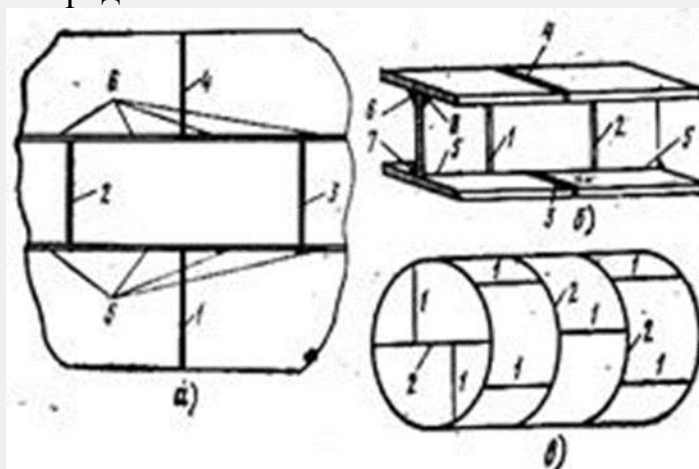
Последовательность наложения швов (1 -8) при сварке:
